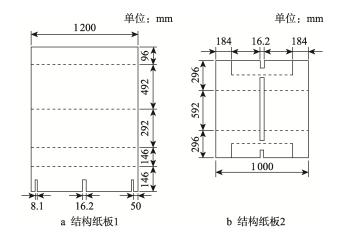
瓦楞纸板托盘的尺寸标注 Fig.2 Dimensioning diagrams of pallet with corrugated board
